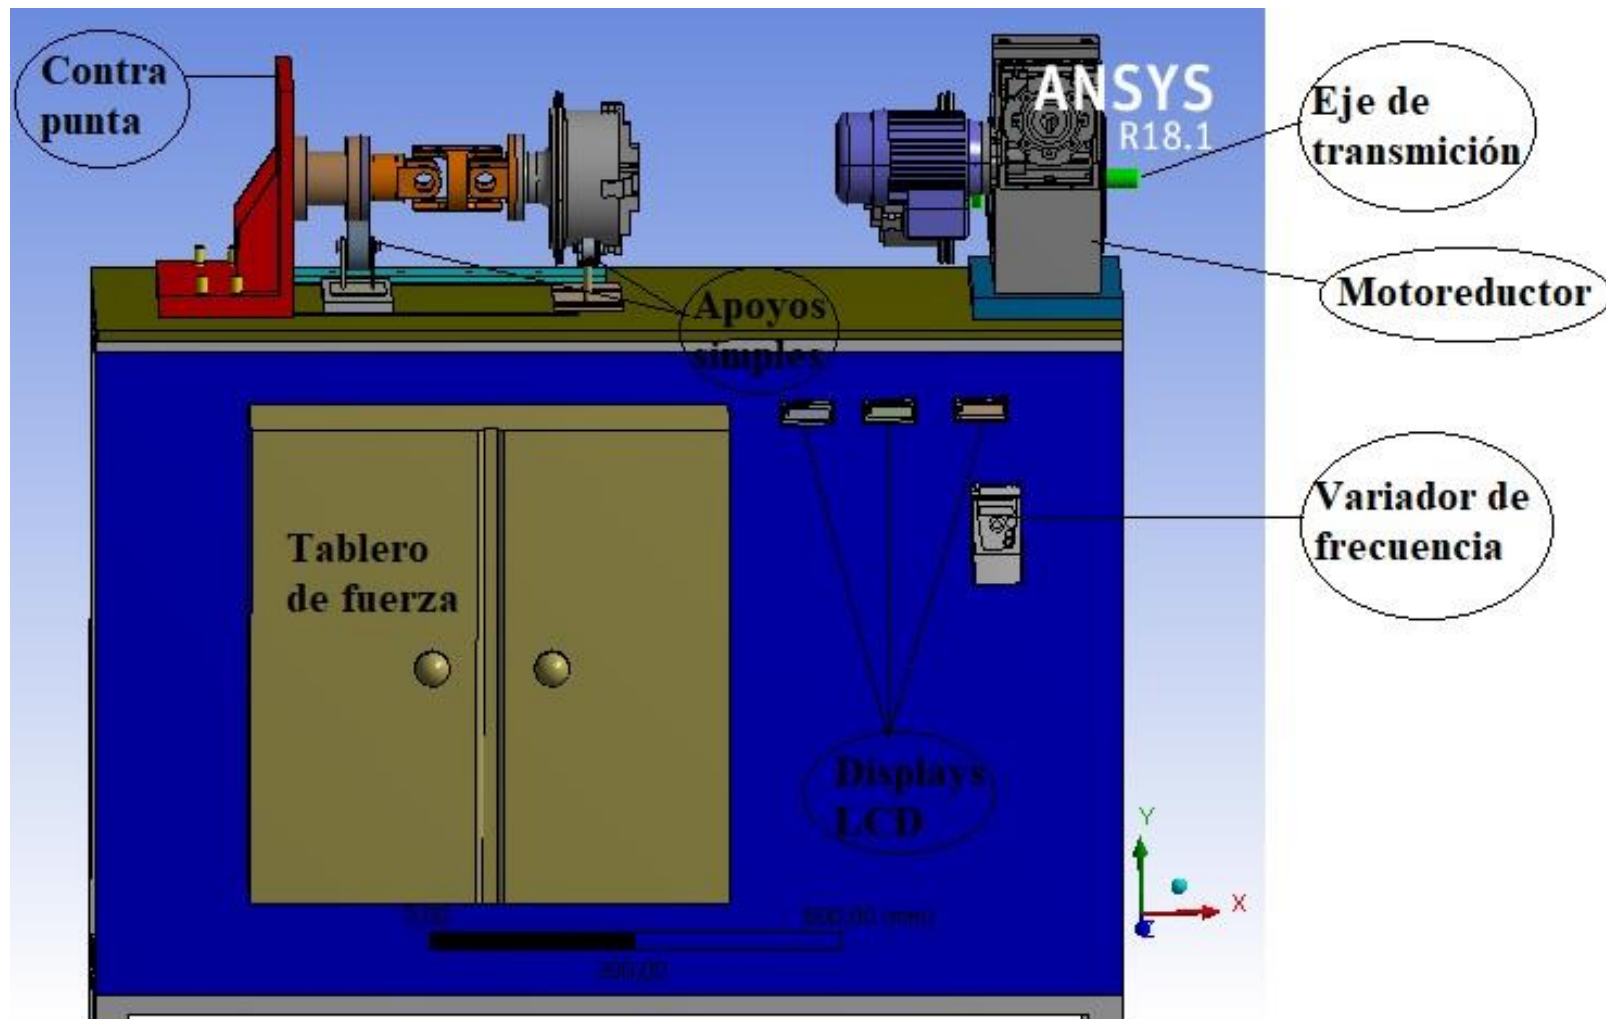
Layout 2D vista lateral del sistema de torsión. Fuente: Elaboración propia.
